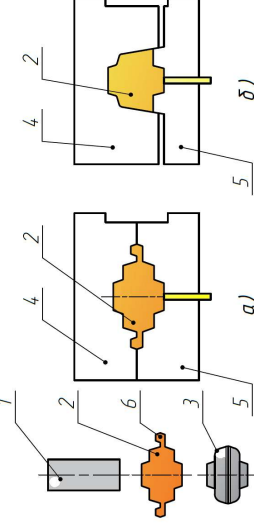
Схеми штамів: а) відкритий б) закритий (1 – заготовка; 2 – виштамповка з облоєм; 3 – виштамповка; 4 – верхня частина штампа; 5 – нижня частина штампа, 6 – облой)
